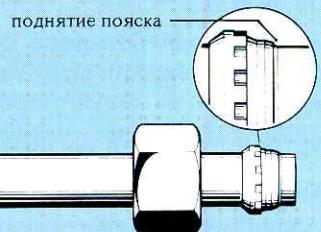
Указания по монтажу резьбовых соединений с врезными кольцами
